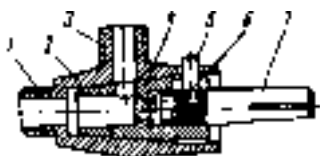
Унифицированный пробковый кран газовой плиты: 1 - штуцер для присоединения к газопроводу; 2 - корпус; 3 - штуцер для присоединения к коллектору; 4 - пробка; 5 - стопорный винт; 6 - пружина; 7 - стержень
